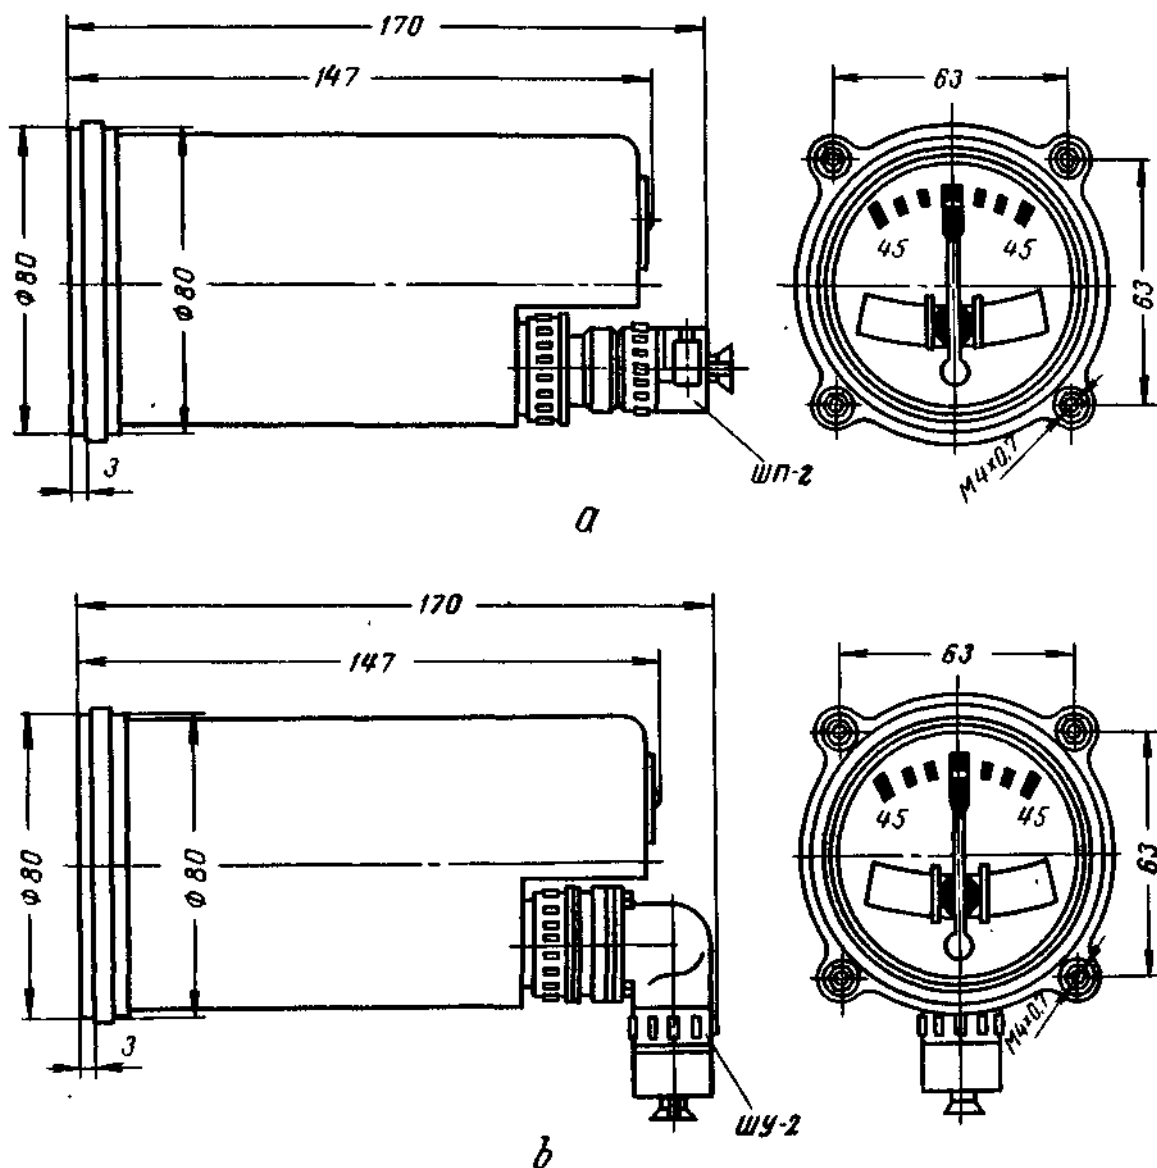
Габаритные и установочные размеры ЗУП-53 и ЗУП-53У:
